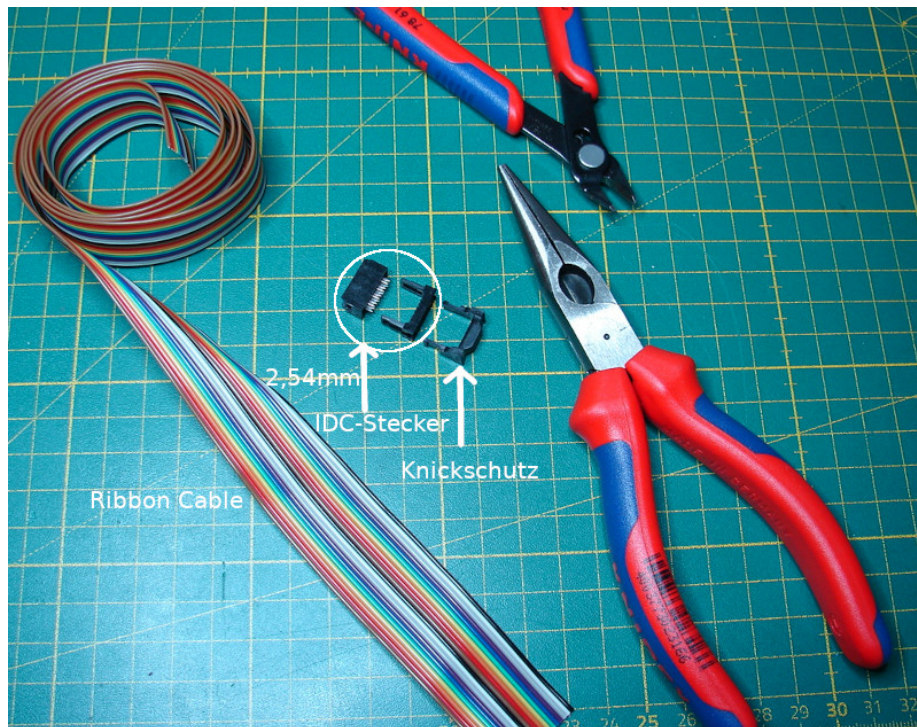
Werkzeug und Ribbon Cable + IDC-Stecker zum selber crimpen
